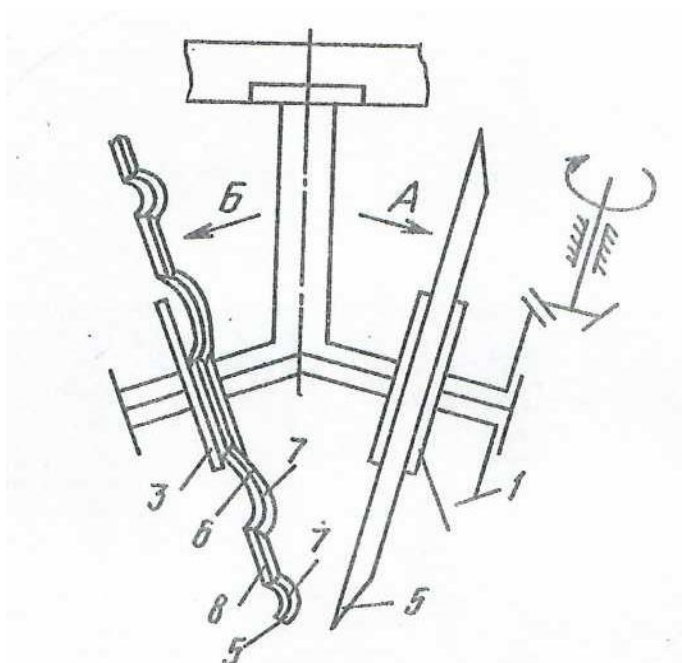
Пристрій для викопування коренеплодів [12], вид спереду
